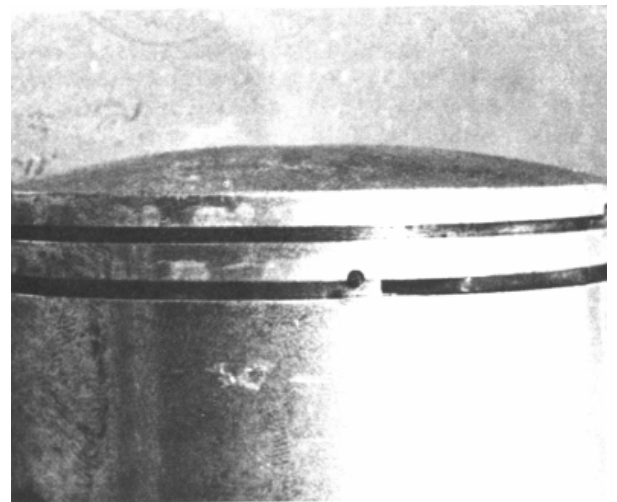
Prüfen, ob die Kolbenringstifte sich nicht gelockert haben
